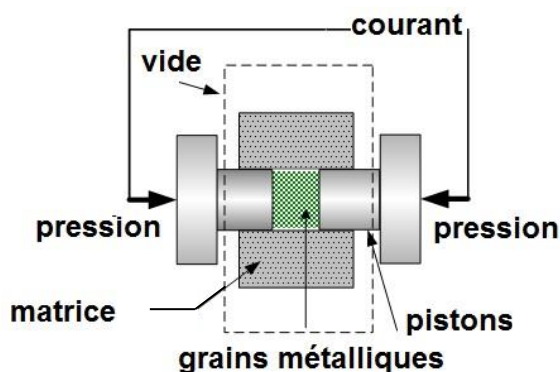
Principe du frittage par SPS ou par Gleeble
